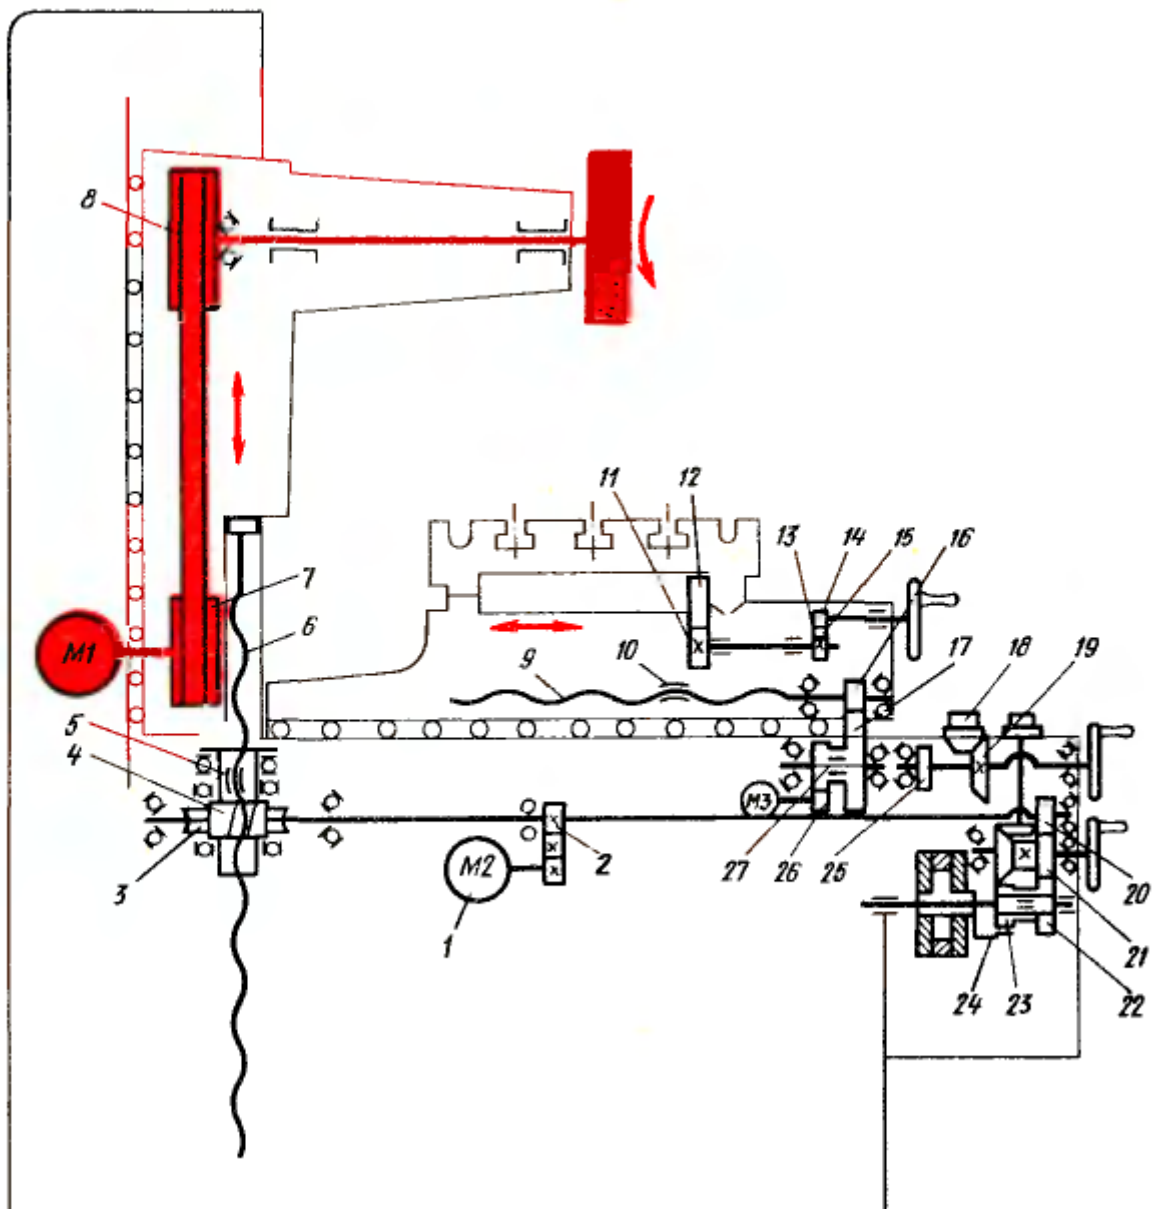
Кинематическая схема плоскошлифовального станка с горизонтальным шпинделем
